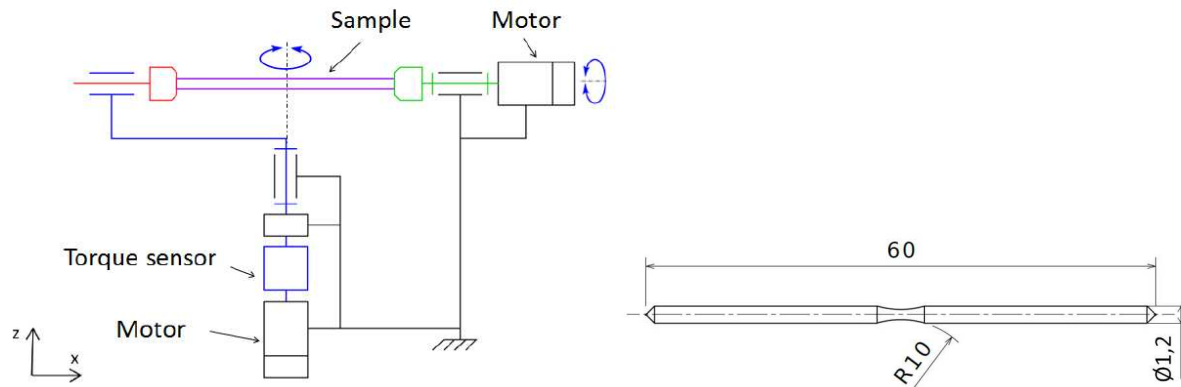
(a) Machine de flexion rotative, (b) géométrie de l'éprouvette diablo.
